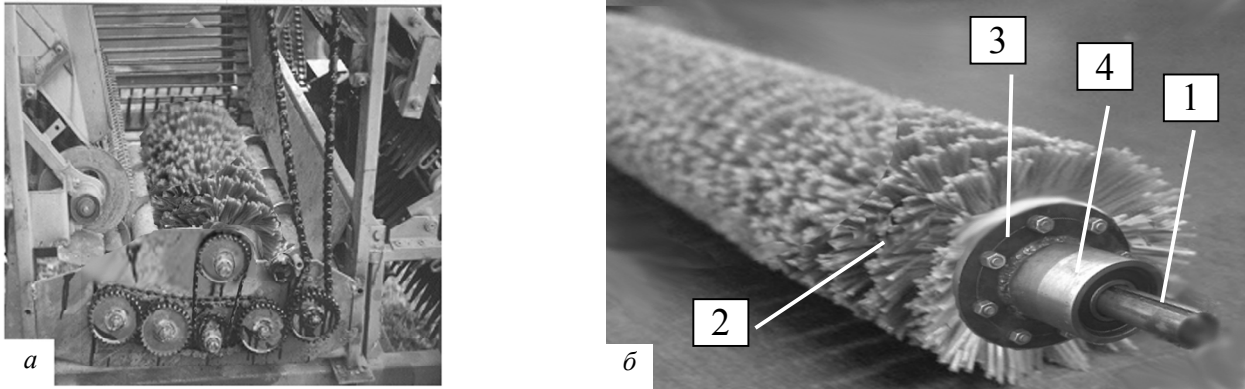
Загальний вигляд: а – ТОС; б – привідного вала з очисними пружними елементами;
